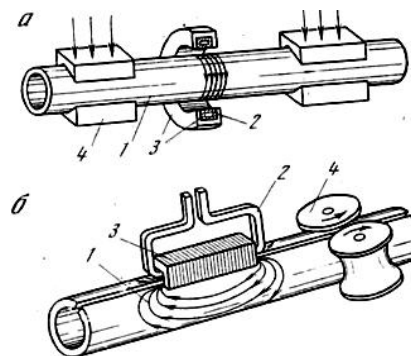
Схемы поперечной (а) и продольной (б) стыковой сварки труб ТВЧ (1 – свариваемые трубы; 2 – индуктор; 3 – магнетрон; 4 – устройство для создания давления в зоне сварки; стрелками обозначены направления протекания индукционных токов в свариваемых частях труб) [16]
